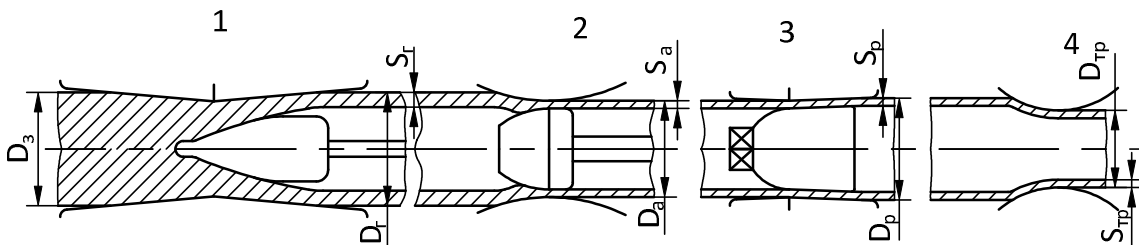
Загальна схема формозміни труби на ТПА з автоматичним станом (з одним прошивним станом): 1 — прошивка заготовки в товстостінну трубу на стані поперечно-гвинтової, 2 — прокатка гільзи в чорнову трубу в автоматичному стані повздовжньої прокатки; 3 — розкатка чорнової труби в розкатному стані поперечно-гвинтової прокатки; 4 — калібровка або редукування труби в безперервному стані [6]
